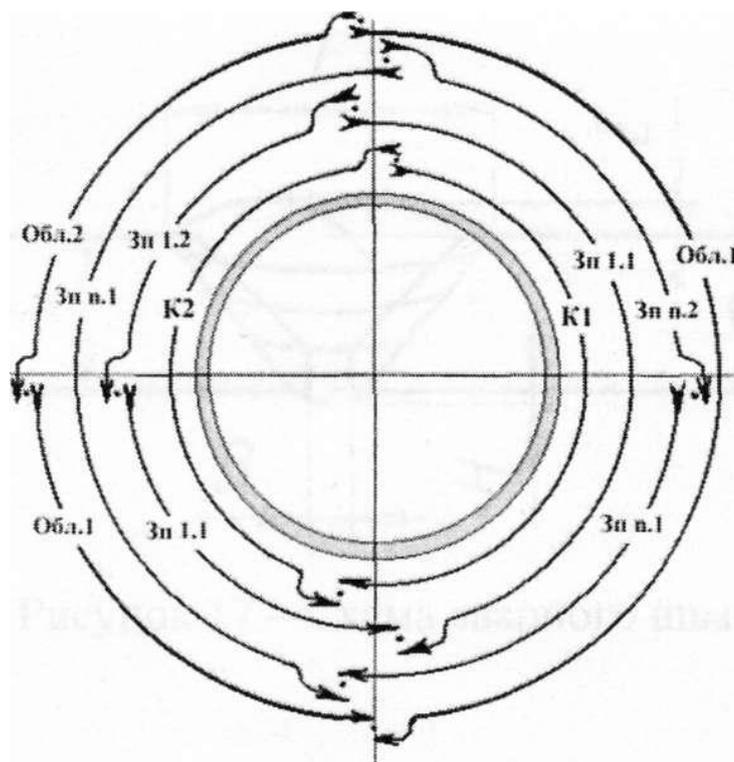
Схема сварки и последовательность сварки отдельных участков шва
